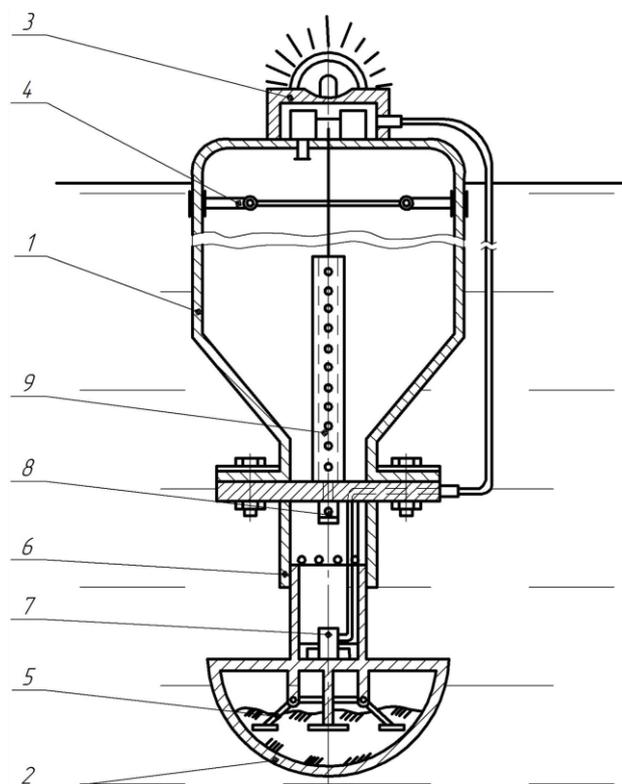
Самовсплывающий грейфер с газогенераторным носителем порохового типа
